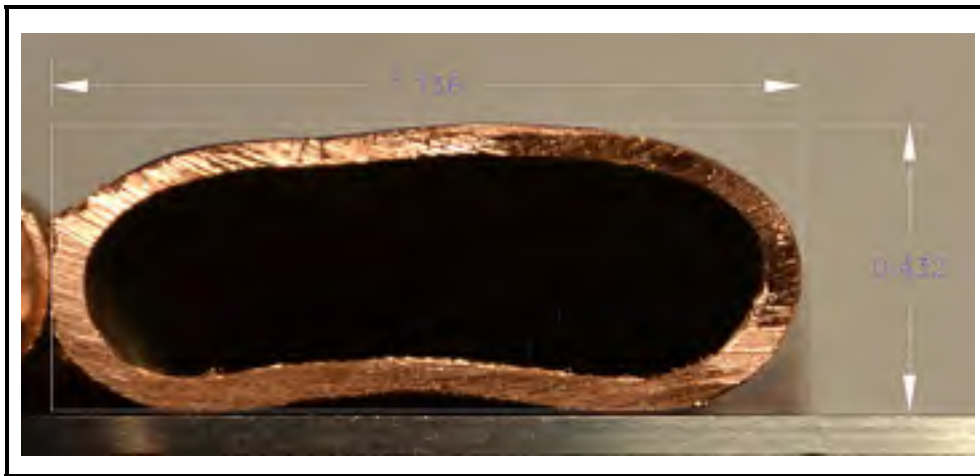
Section du tube serpentin préformé et enroulé lors du test
